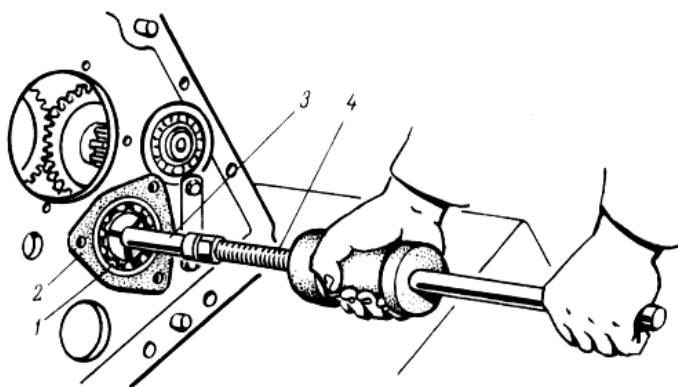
Випресування підшипника проміжного вала: 1- підшипник; 2- гніздо підшипника; 3- цанга; 4- інерційний знімач
